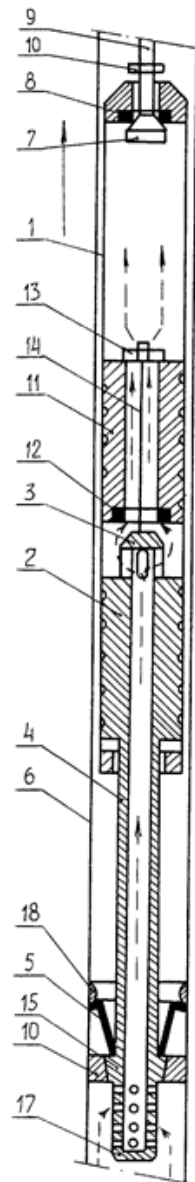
Скважинный штанговый насос с управляемыми клапанами
